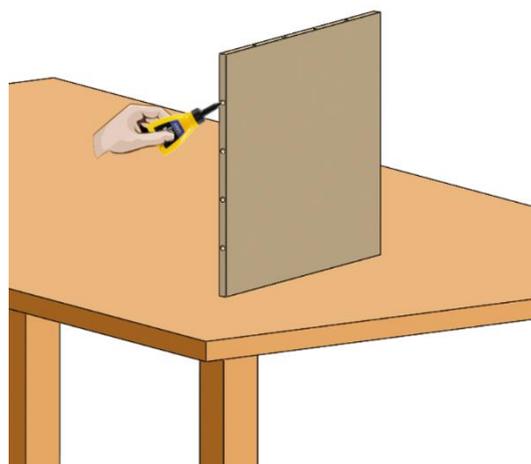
Paso 1 del ensamblaje del cajón (conjunto 2)
